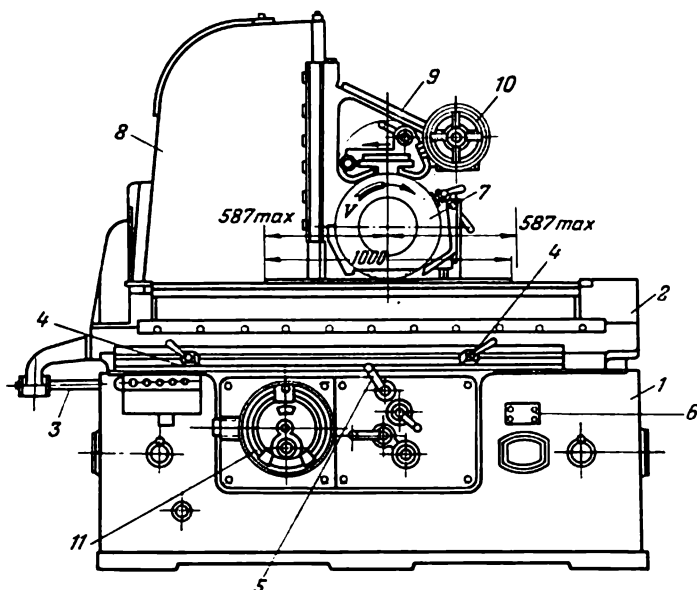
Vue d'ensemble d'une rectifieuse plane
